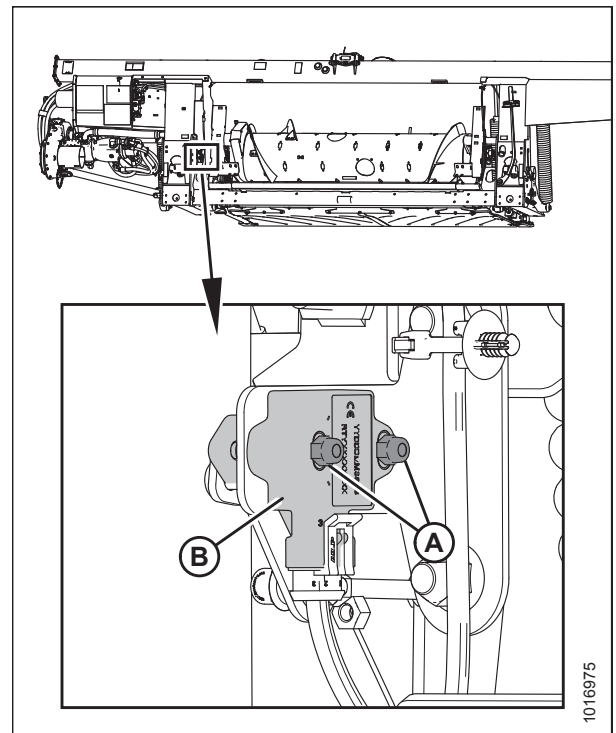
Kit opcional de 2 sensores: sensor izquierdo
